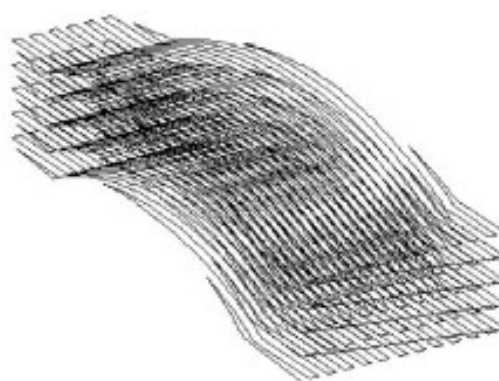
Exemplo de um processo “*Deposition Shaped Manufacture*” (SDM)
